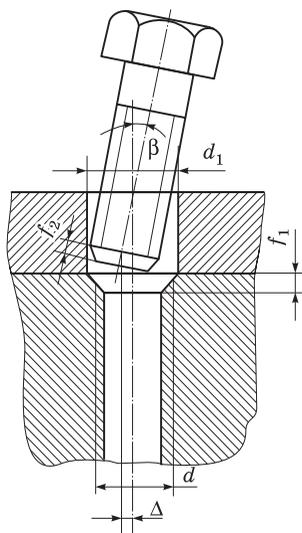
Схема к расчету погрешностей сборки резьбового соединения
